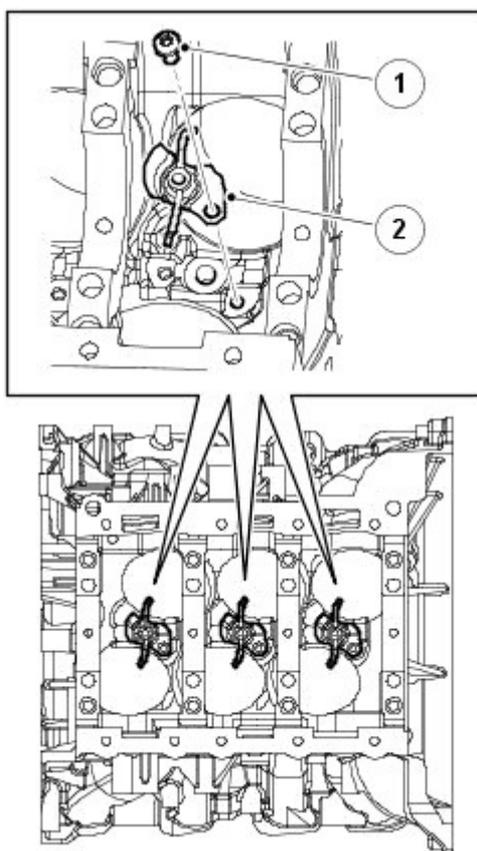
Форсунки охлаждения поршней дизельного двигателя 2.7 TD V6
